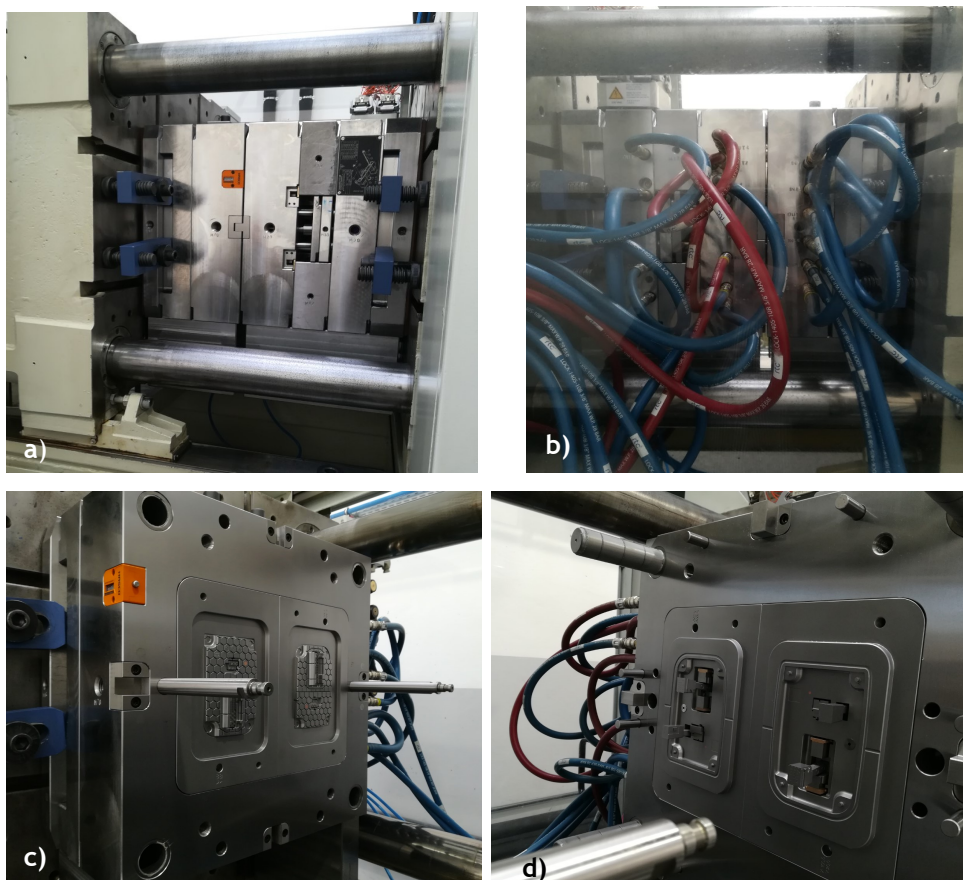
Molde montado na máquina de injeção de plástico. a) Molde visto do lado do operador. b) Molde visto do lado oposto ao operador. c) Lado da extração (bucha). d) Lado da injeção (cavidade).
